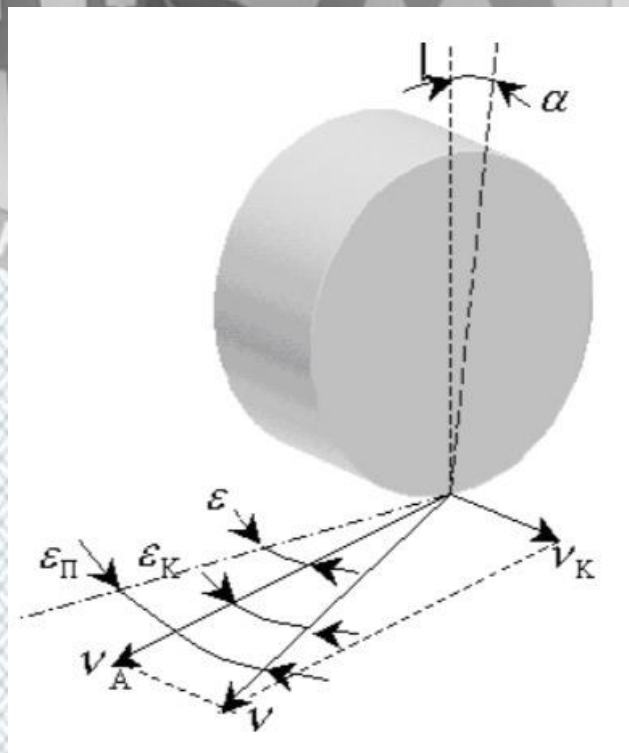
Схема кочення колеса з кутами сходження ε і розвалу α
